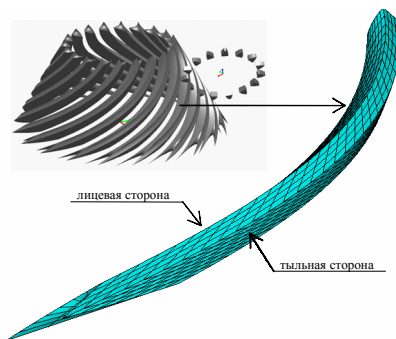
КЭМ зуба колеса двухпараметрической передачи
